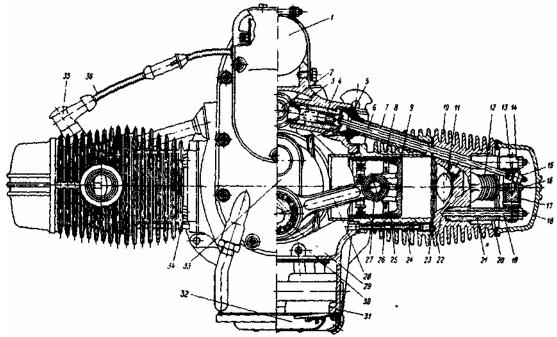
Двигатель М67-36 мотоцикла "Урал" (поперечный разрез):
